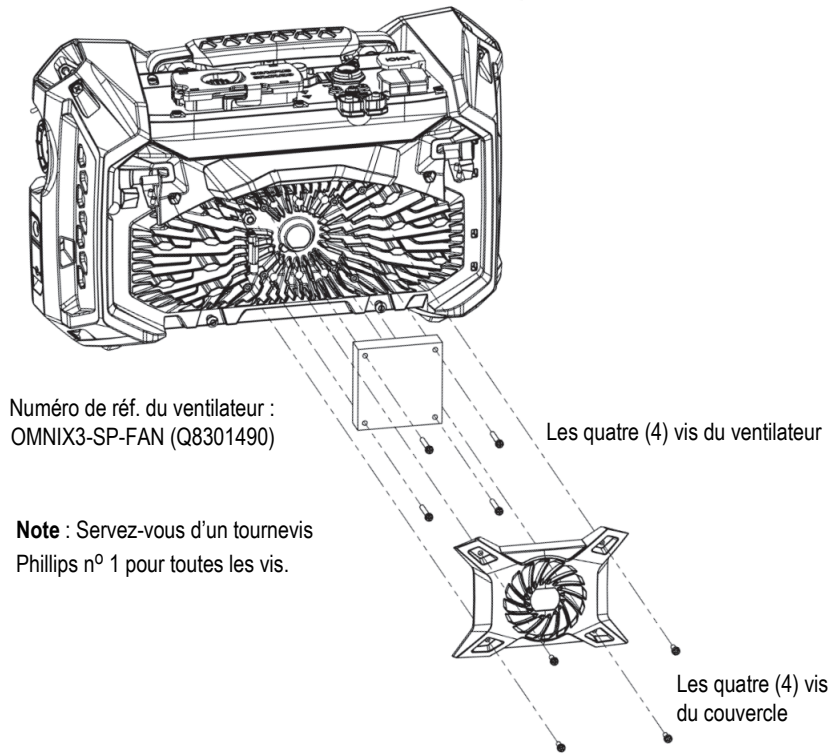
Assemblage du ventilateur et des pièces du couvercle
